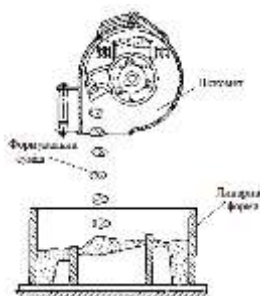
Формувальний піскомет для габаритних форм
